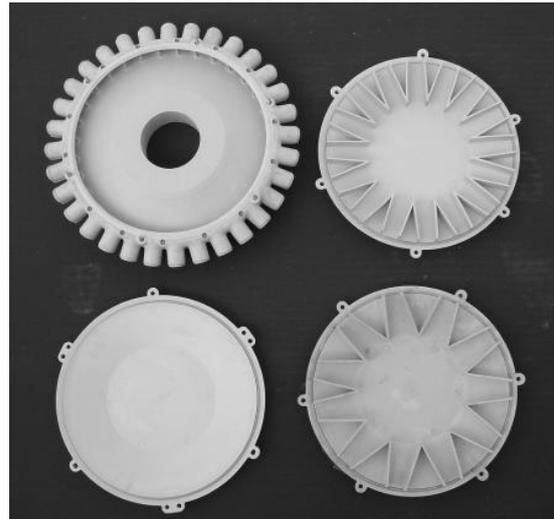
distribuidor 32, cubierta lisa del distribuidor 32, cubierta de reducción 32/16 y 32/11
